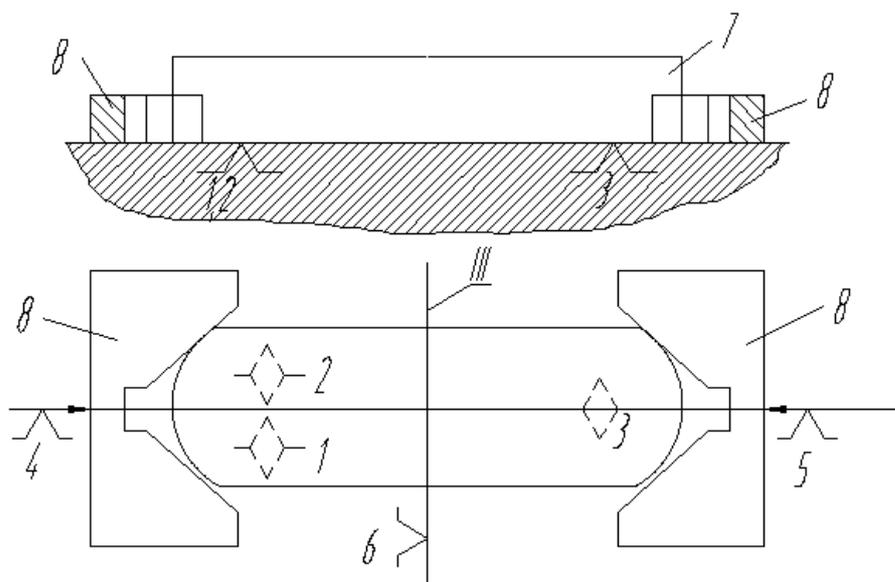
Примеры скрытой и явной базы: *I* - установочная явная база заготовки; *II* - направляющая скрытая база заготовки; *1...6* - опорные точки; *7* - заготовка; *8* - губки самоцентрирующих тисков.
